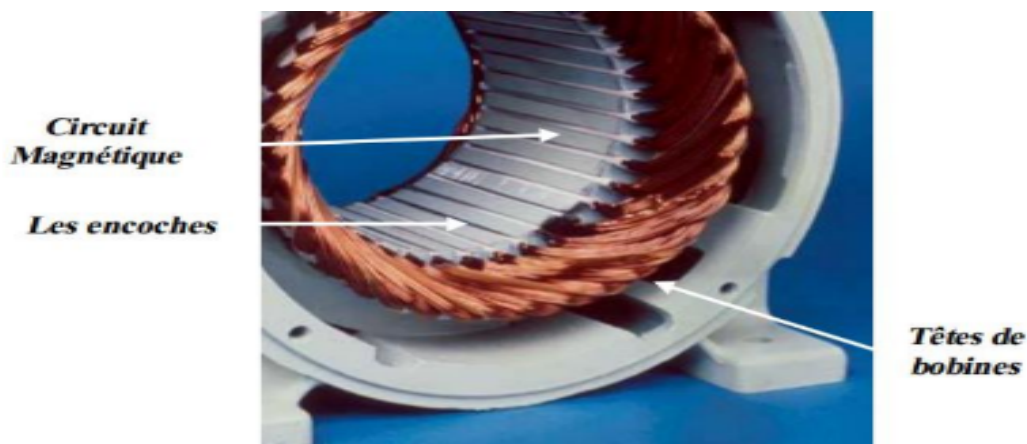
Stator d’une machine asynchrone [37].
